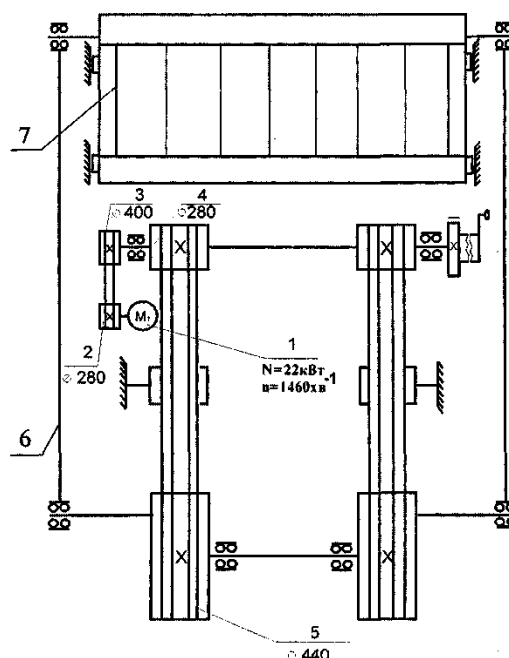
Кінематична схема механізму різання пилогами РТ-2: 1 - електродвигун механізму різання; 2, 3 - шківні привода; 4, 5 - шківні контрпривода; 6 - шатун; 7 - пилкова рамка
